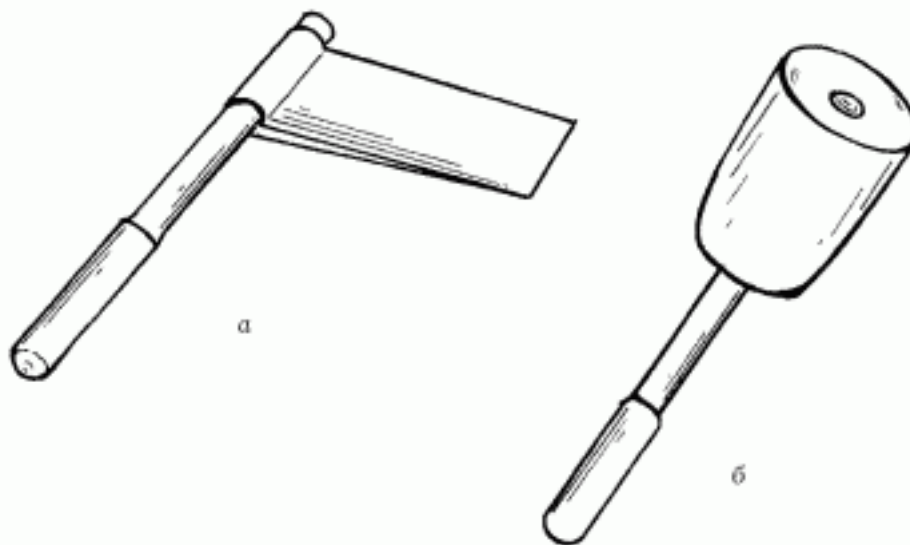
Приспособления для изготовления гонта в домашних условиях: а – колющее лезвие; б – колотушка.
